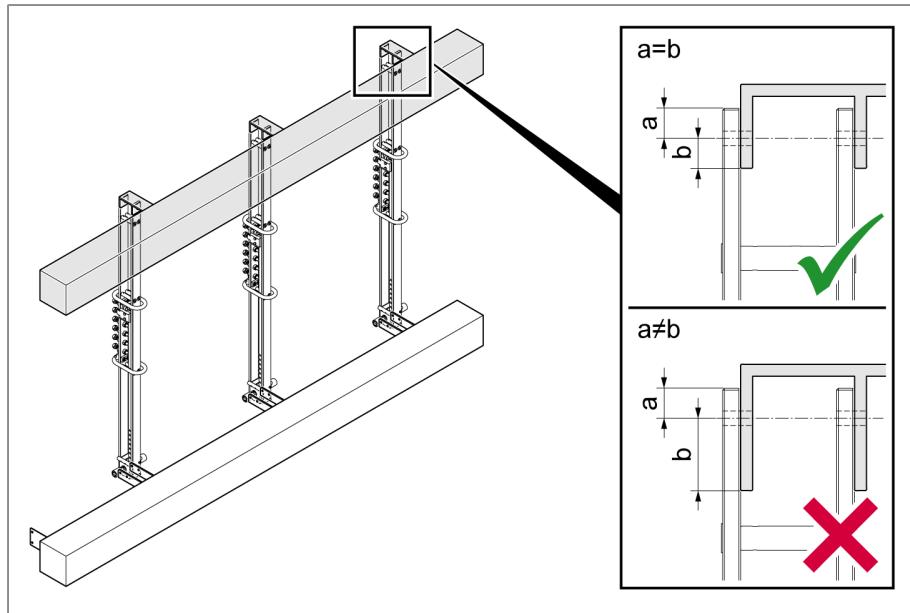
Крепежное приспособление на держателе, устройство ПБВ с фронтальным расположением контактов
